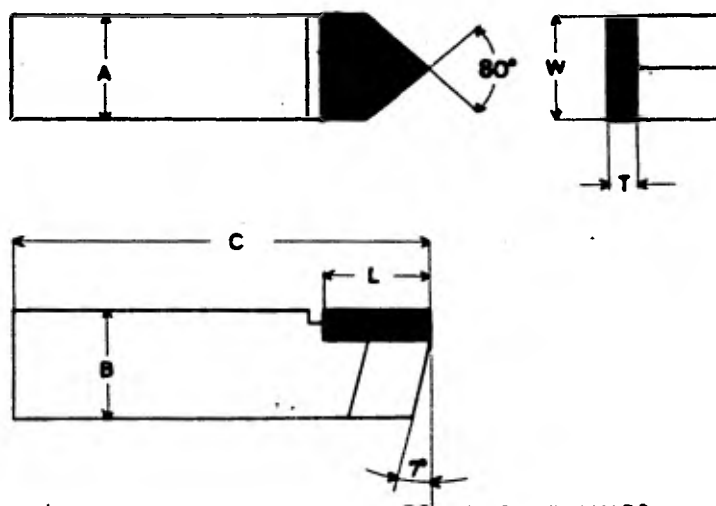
BURIL PARA COPIADO Y CHAFLANADO.
